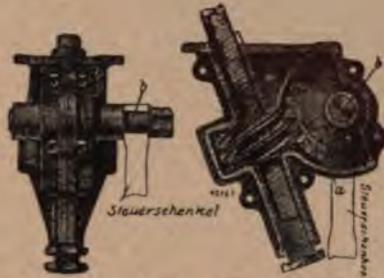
Ansicht einer Steuerung durch Schnecke und Zahnrad.
